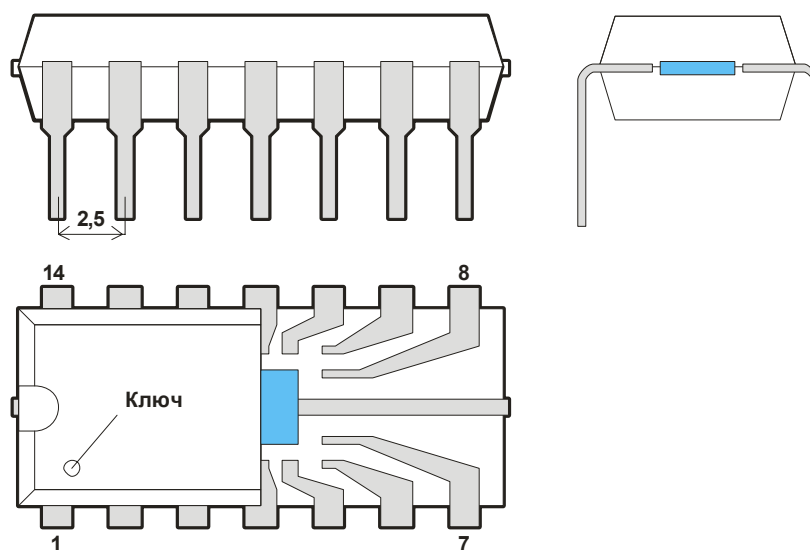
Конструкція пластмасового корпусу 2102
